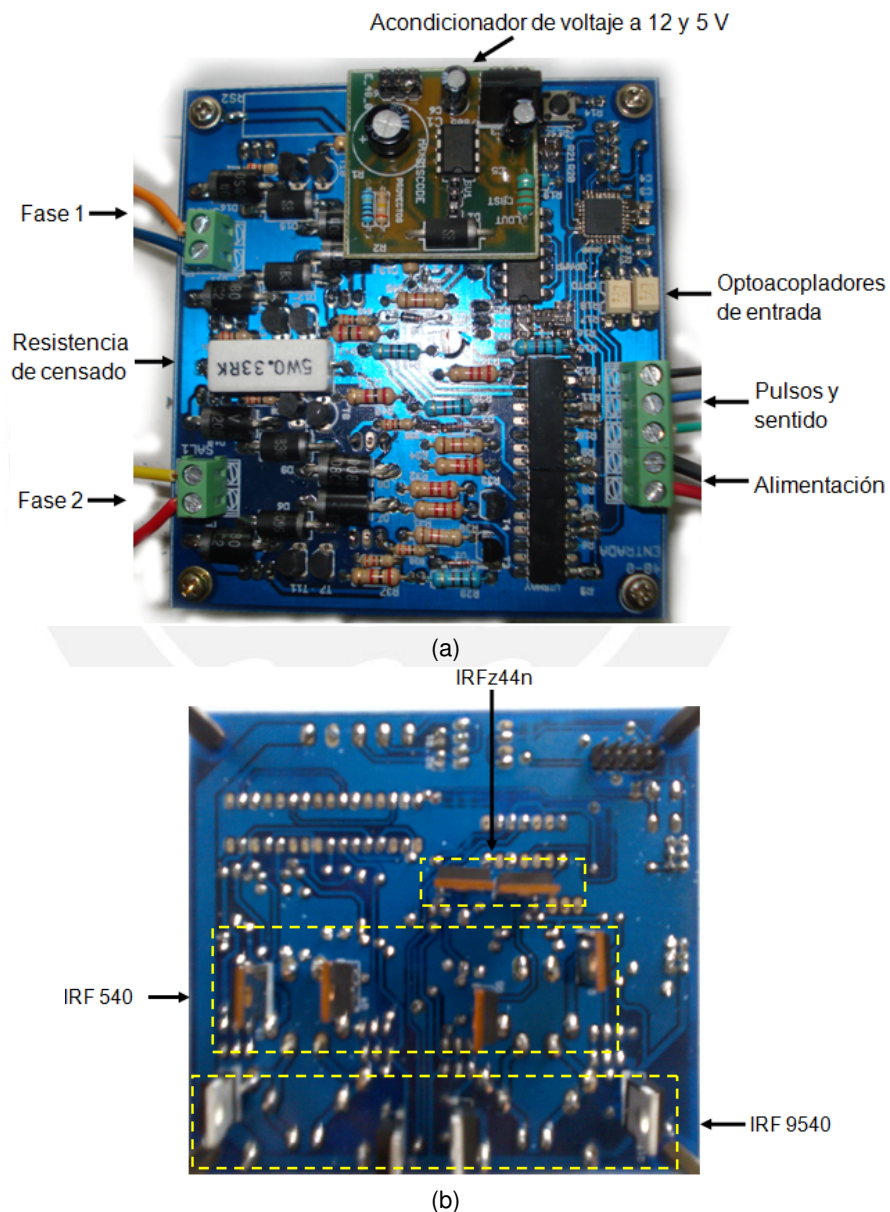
Driver de motor paso a paso implementado. (a) Vista frontal de la tarjeta Driver. (b) Vista posterior de la tarjeta Driver.
